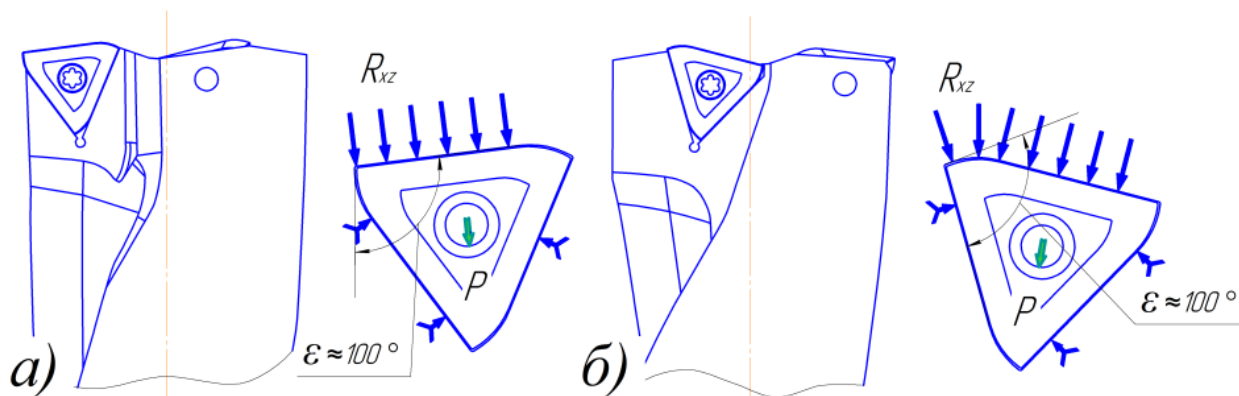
Схематичное изображение базирования, нагружения и закрепления режущих пластин новой формы: а – периферийной и б – центральной в корпусе сборного сверла
